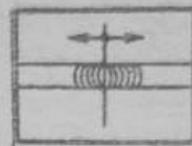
Сварка швов средней длины от середины к концам шва
